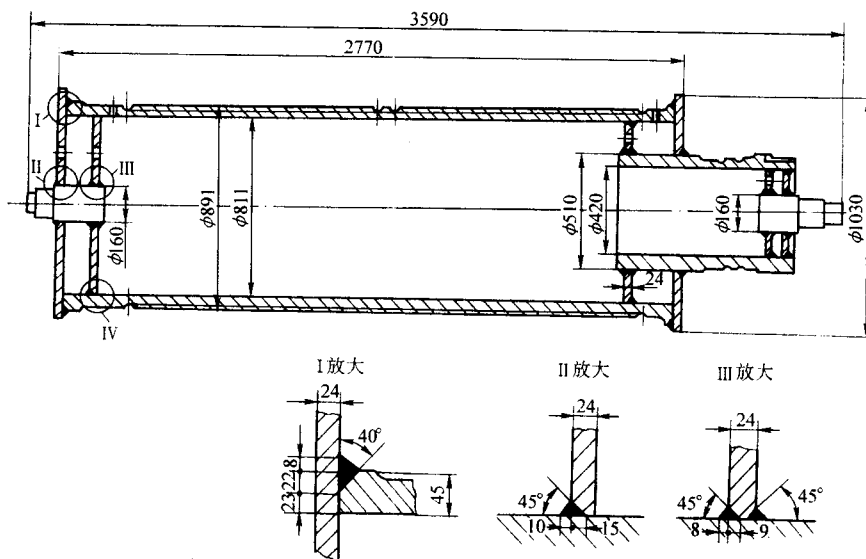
70/20 t 起重机卷扬筒的焊接结构
